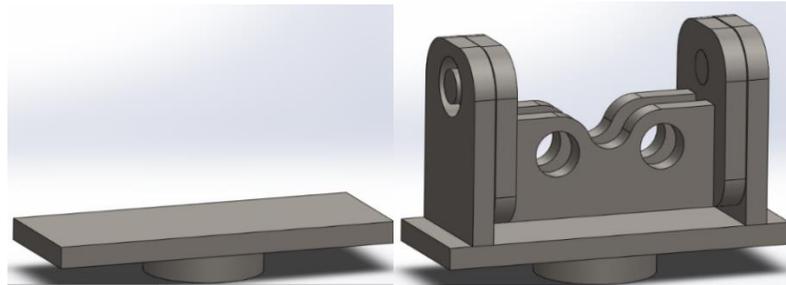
Placa superior (Pieza N° 1 de ensamble). Fuente: Elaboración propia.
